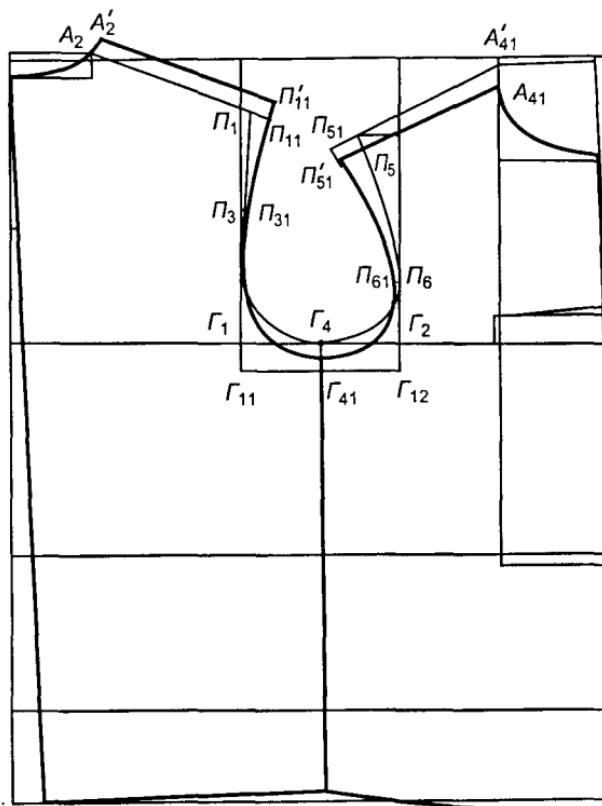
Построение чертежа основы конструкции плечевого изделия с рукавами рубашечного покрова и овальной проймой
